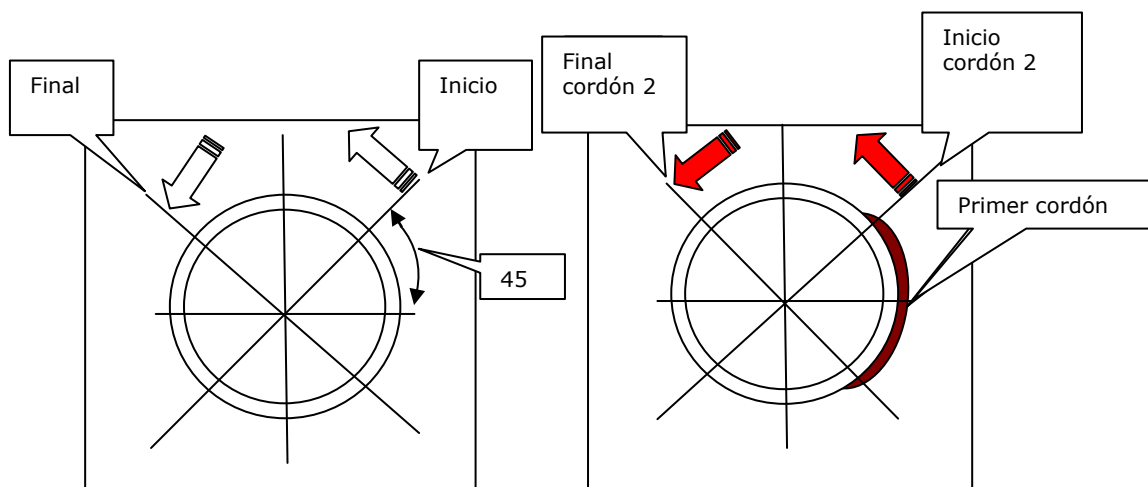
Posición del ensamble para realizar la soldadura en posición horizontal.
